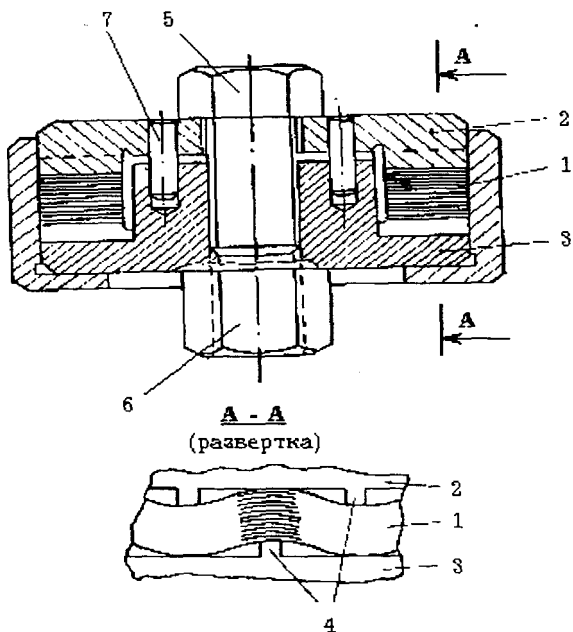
11. Схема приспособления для формирования гофров в пакете шайб и их термофиксирования: 1 - пакет шайб; 2 - пуансон; 3 - матрица; 4 - выступы на пуансоне и матрице; 5 - болт; 6 - гайка; 7 - направляющие штифты.
